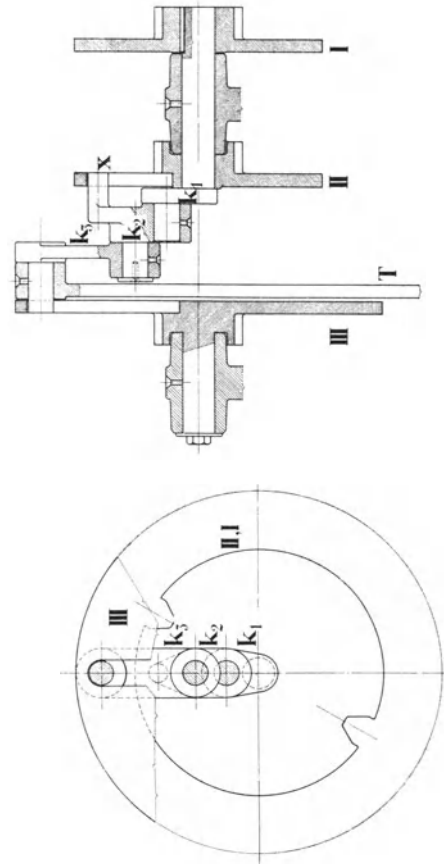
195. Kurbelmechanismus des Prof. Ing. B. Vlček für einen Sechskastenschützenwechsel.
